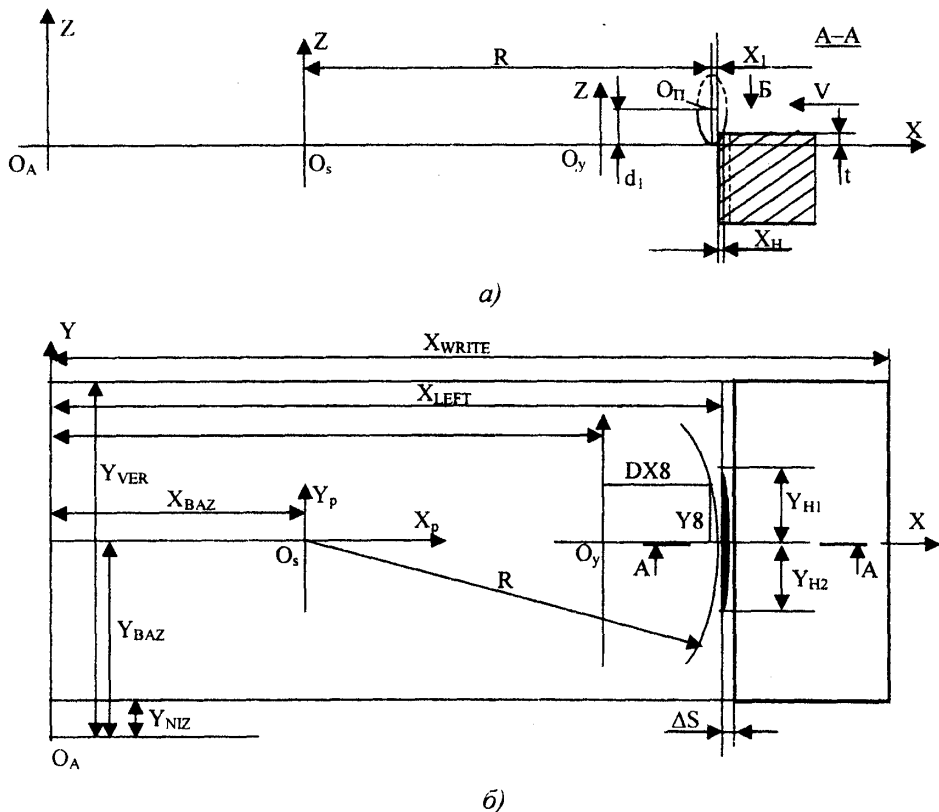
Схема врізання ножа в поверхню заготовки:
